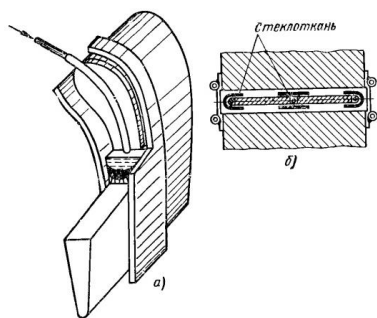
Схема электрошлаковой сварки плавящимся мундштуком:
